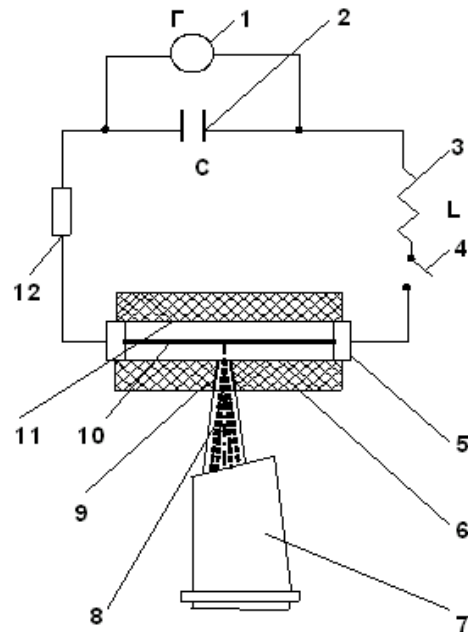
Схема імпульсного плазмотрона з квазіізохорною вибуховою камерою:
